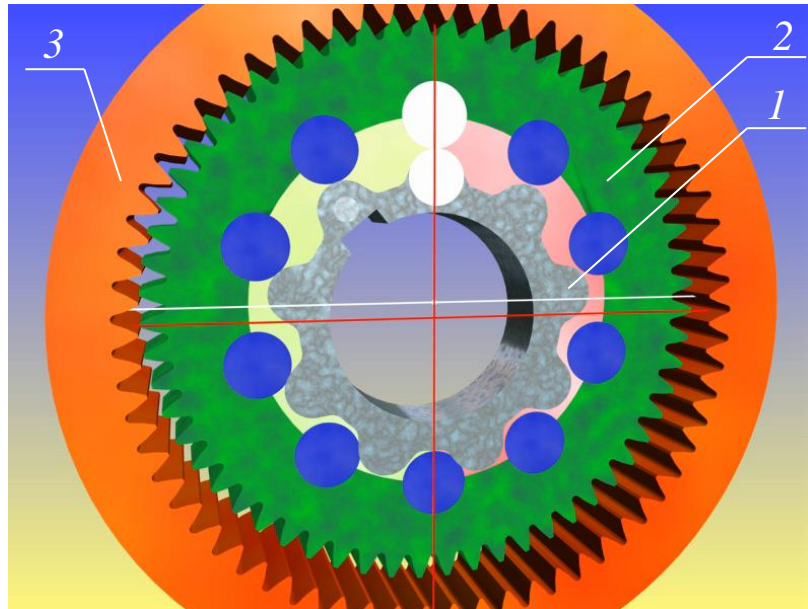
Компенсація планетарного руху роторів за допомогою зовнішнього зубчастого зачеплення: 1 – внутрішній ротор (сонячна шестерня); 2 – зовнішній ротор (сателіт); 3 – корпус (коронна шестерня)
